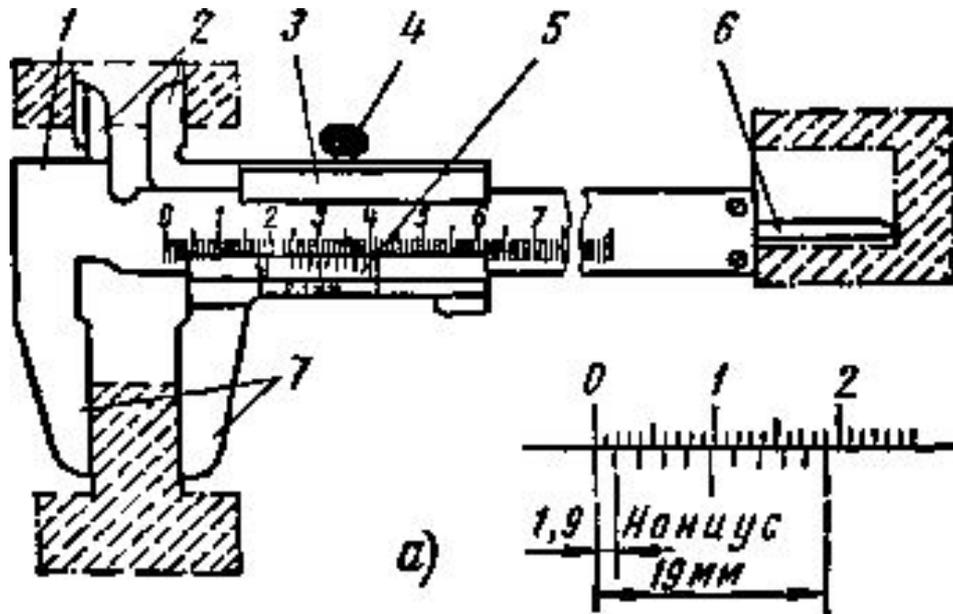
Штангенциркуль: а — штангенциркуль ШЦ-1: 1 — штанга, 2, 7 — губки. 3 — подвижная рамка. 4 — зажим, б — шкала нониуса, б — линейка глубиномера; б — нониус
